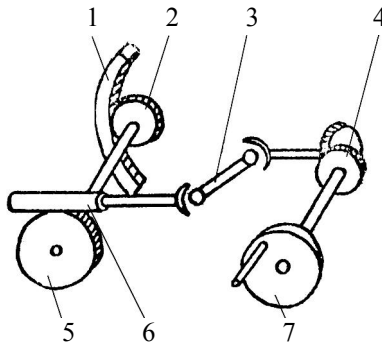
Схема секторного механізму із внутрішнім зчепленням корінної шестерні:
